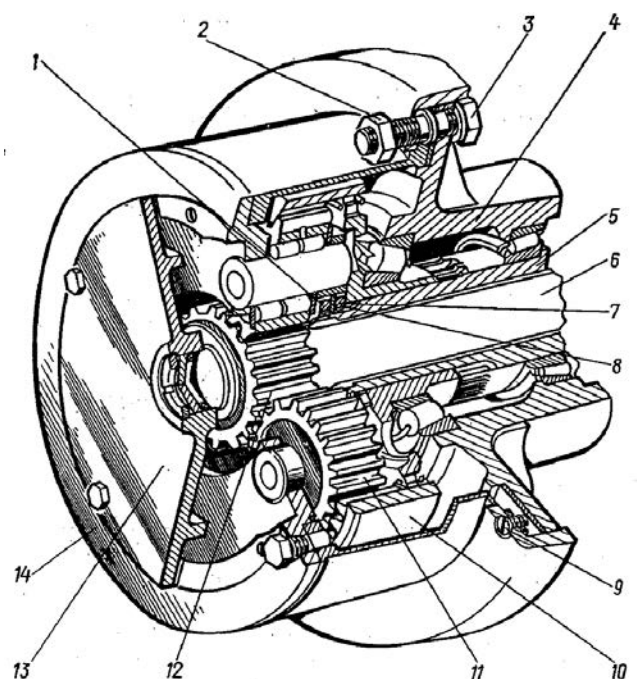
Колесный редуктор: 1 — контргайка; 2, 3, 7 — гайка; 4 — картер; 5 — ступица; 6 — полуось; 8 — шайба стопорная; 9 — винт; 10 — шестерня эпициклическая; 11 — сателлит; 12 — шестерня солнечная; 13 — крышка; 14 — водило
